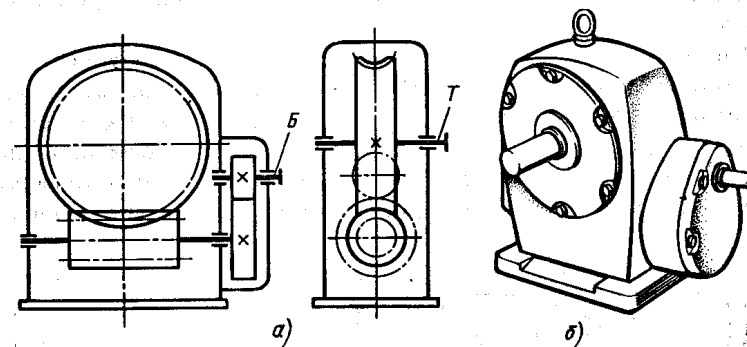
Двухступенчатый зубчато-червячный редуктор:
